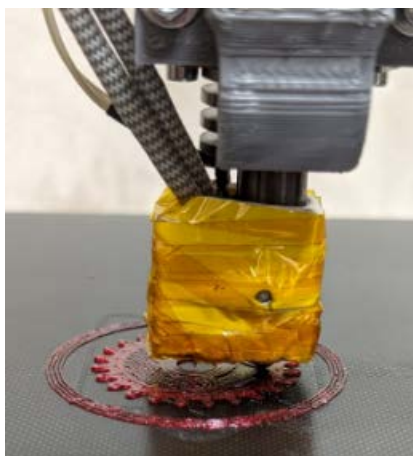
Нагрівальний блок з тепловою ізоляцією
